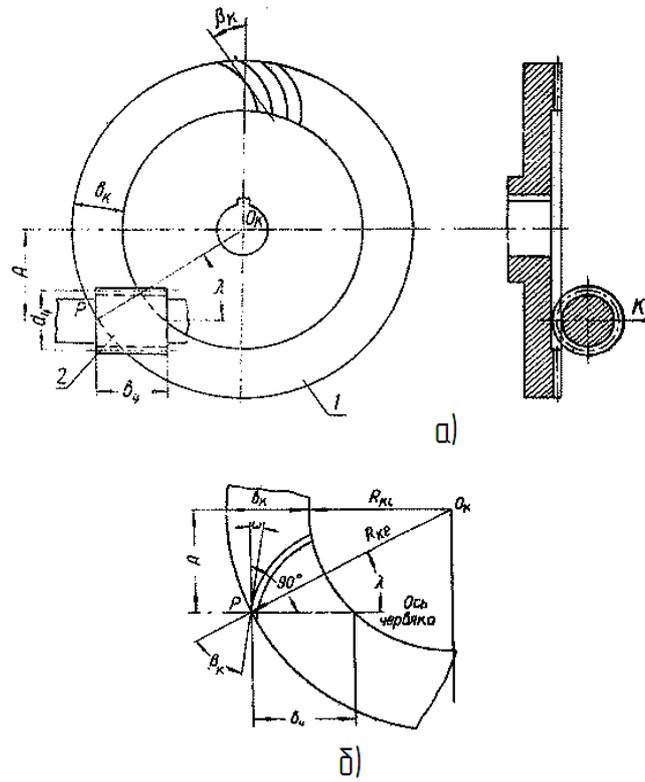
Способ нарезания плоского зубчатого колеса: 1 – плоское колесо; 2 – цилиндрическая червячная фреза
